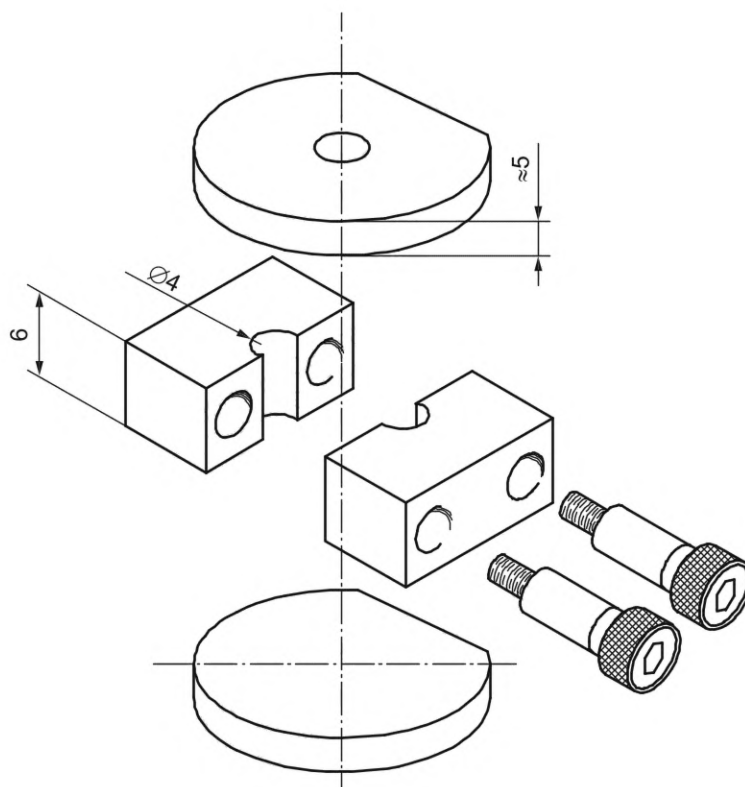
Форма для изготовления образцов для испытания на прочность при сжатии
